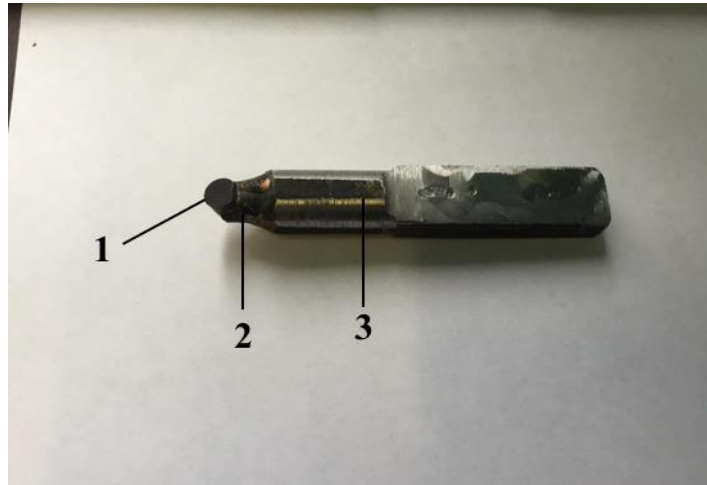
Резец *PDC*: 1 – вставка *PDC*; 2 – сварочное соединение; 3 – резец.
